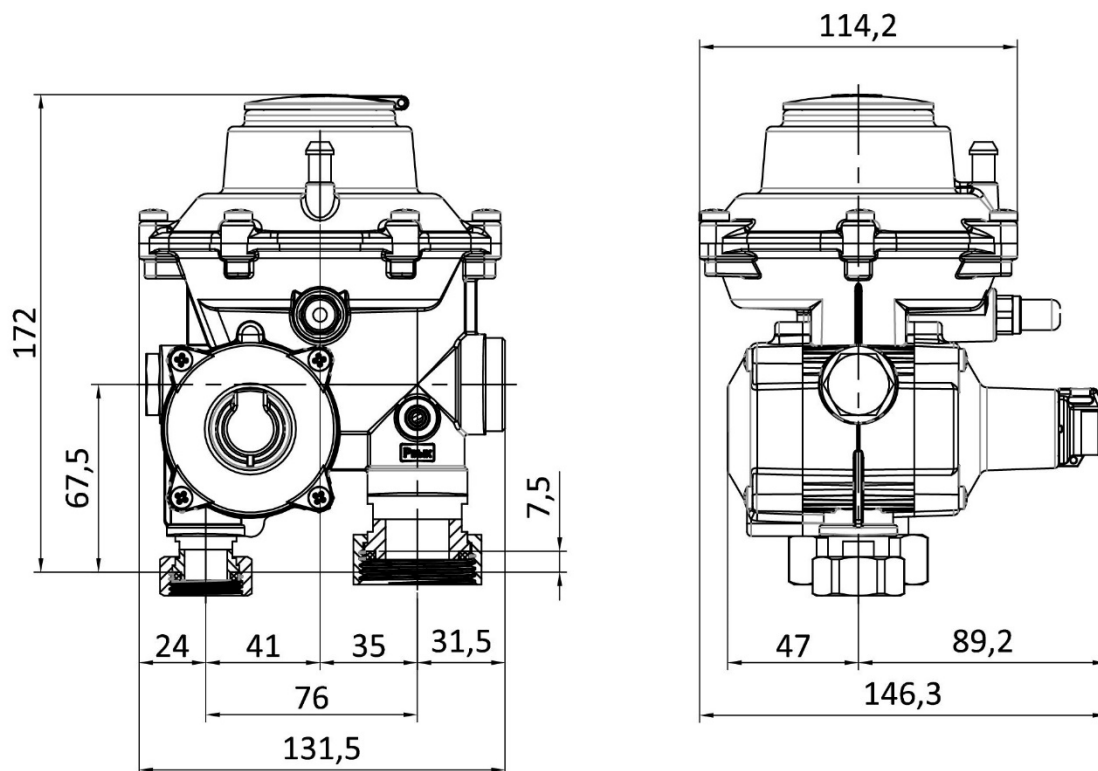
Габаритные размеры регуляторов давления «РЕД-1»
